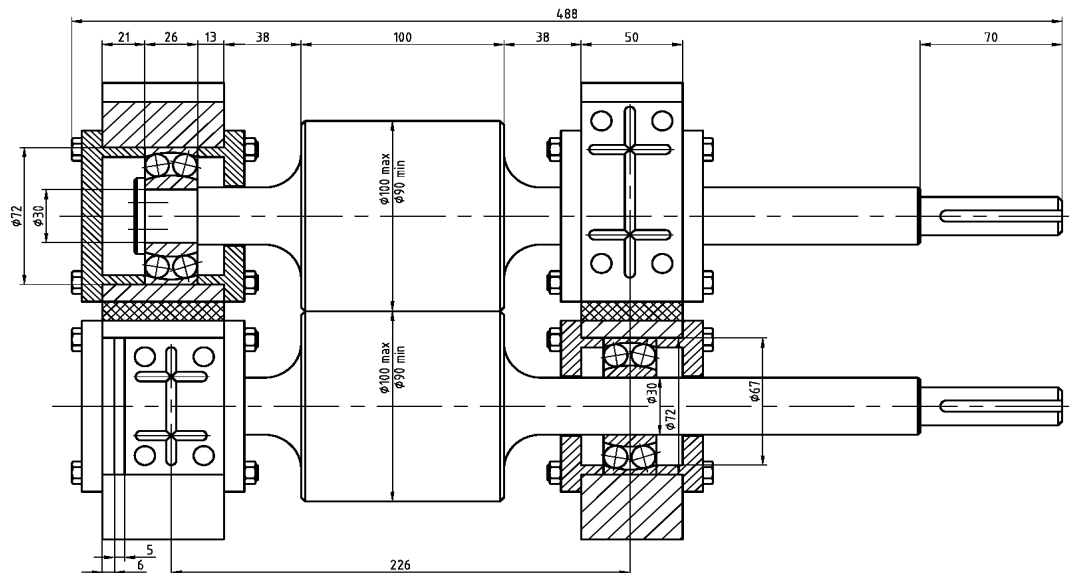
Конструкція вузла робочих валків лабораторного прокатного міні-стану з діаметром валків 260 мм
